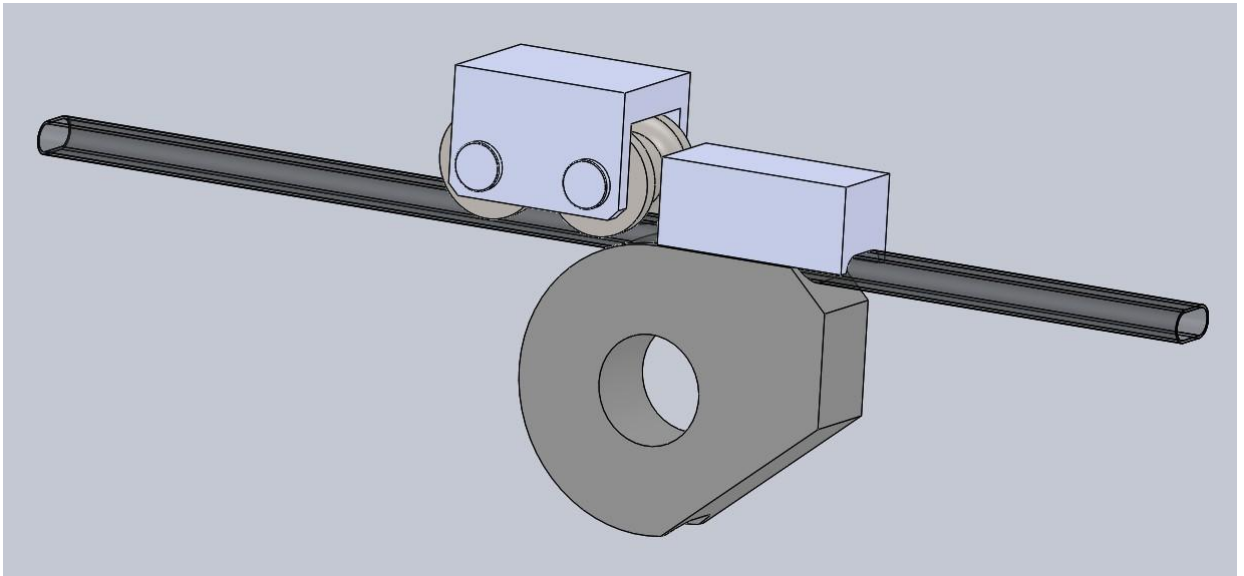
Макет схеми механізму гнуття заготовки
